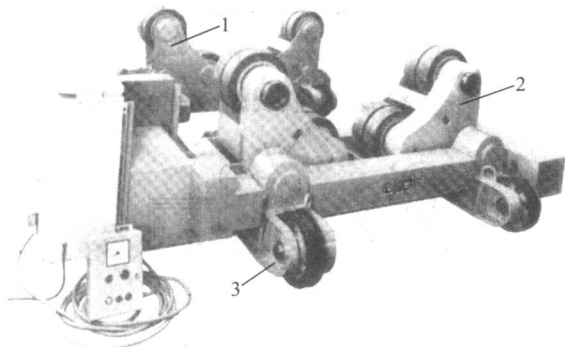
带有行走机构的焊接滚轮架
